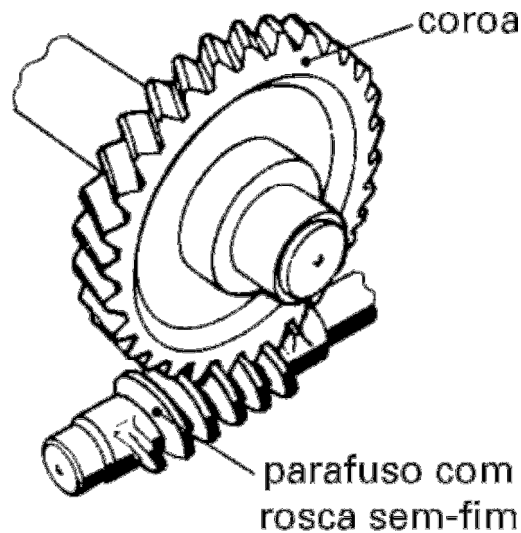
Engrenagem Parafuso com rosca sem fim
